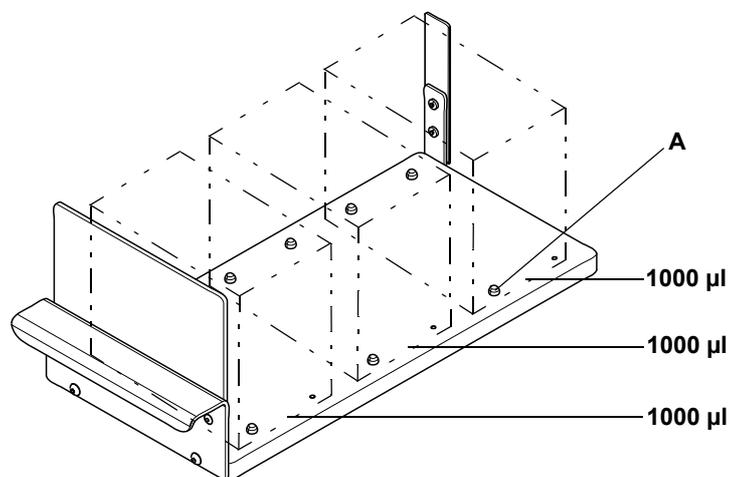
Support pour racks d'embouts jetables (3 racks d'embouts de 1000 µl)
